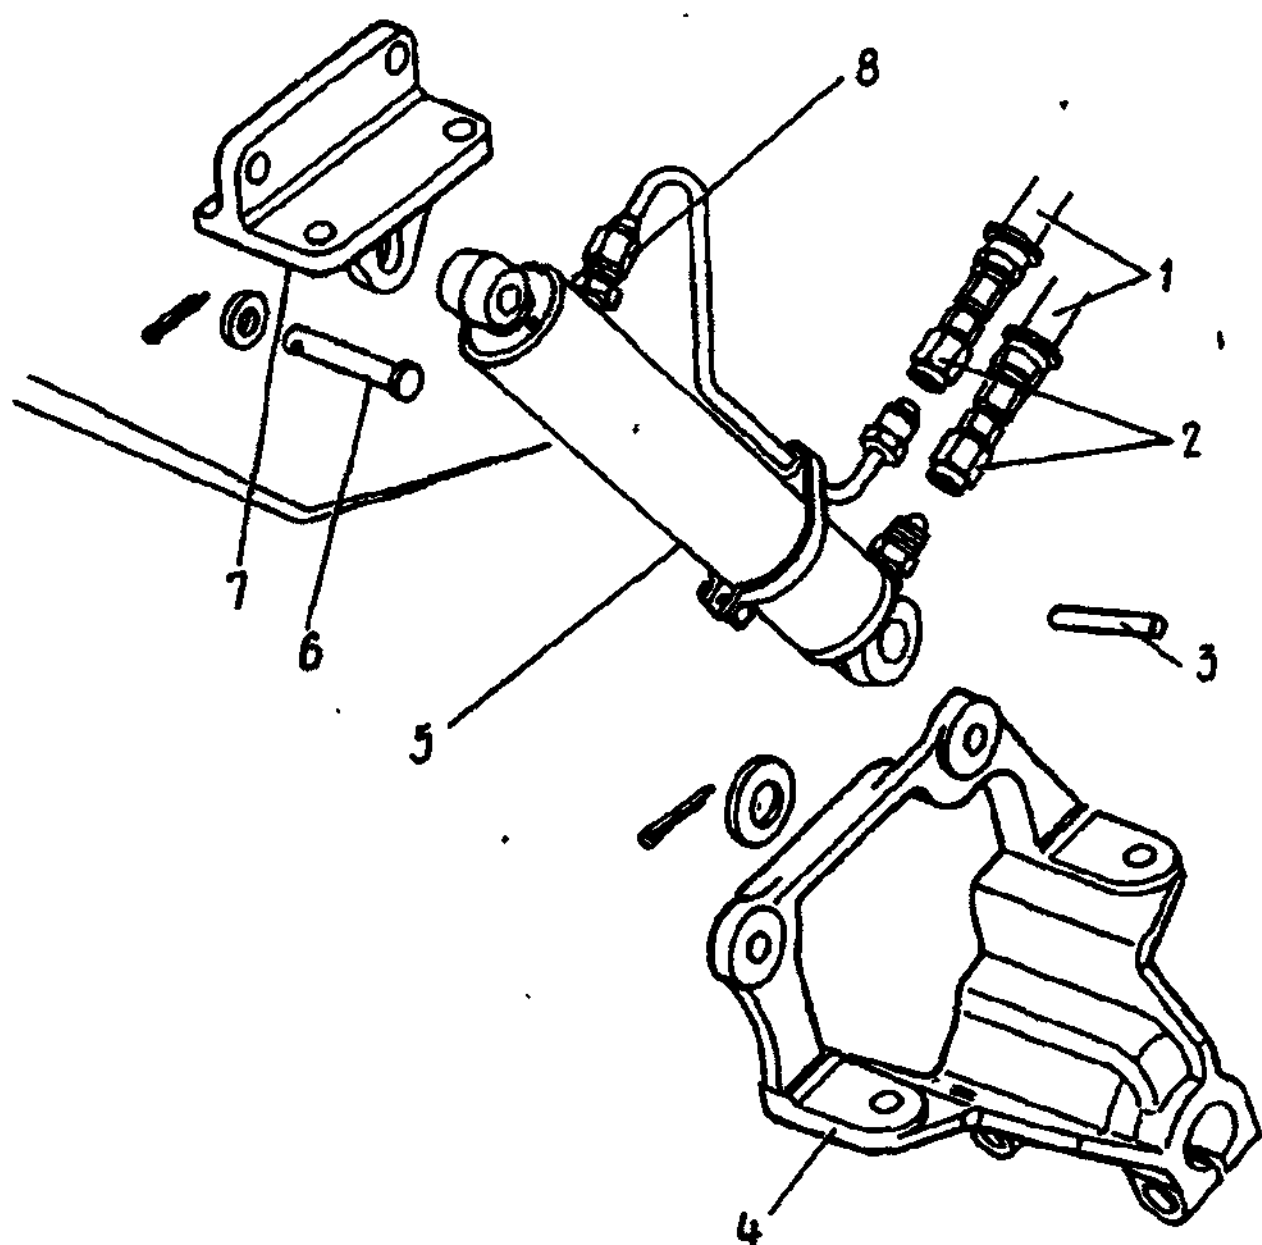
Гидроцилиндр механизма опрокидывания кабины:
